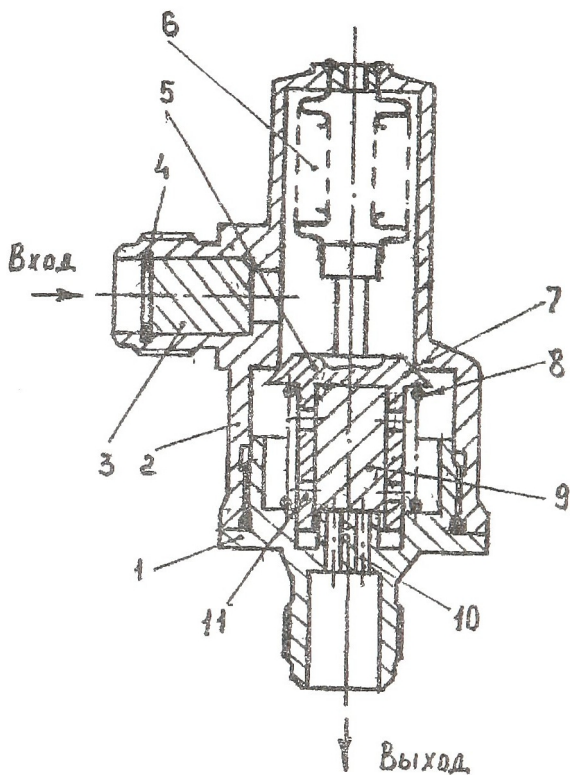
Малошумный предохранительный клапан: 1,2 – корпус; 3 – фильтр; 4 – стопорное кольцо; 5 – конический затвор; 6 – разгрузочный сильфон; 7 – седло; 8 – пружина; 9 – цилиндр из МР; 10,11 – перепускные каналы
